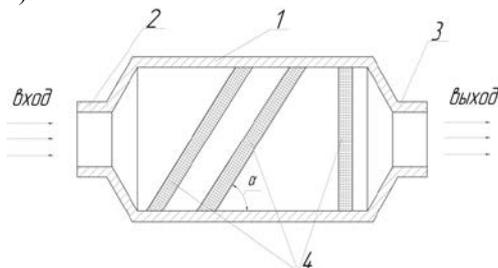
Сетчатый искрогасителя: 1 – корпус; 2 – подводный патрубок; 3 – отводящий патрубок; 4 – пакет газораспределительного аппарата, установленный под углом $\alpha = 55-65^\circ$
